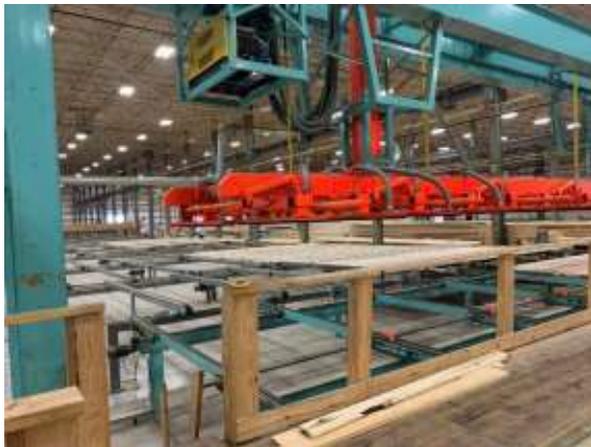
Sistema de apilado por vacío para configurar las capas de paneles CLT
